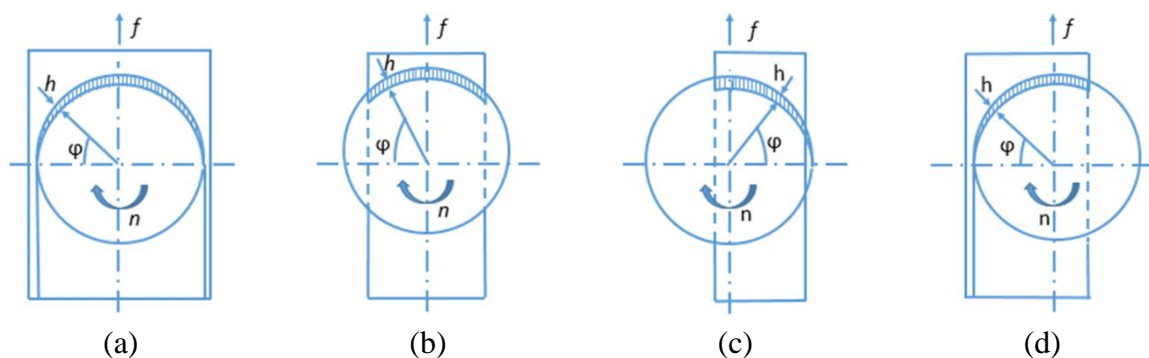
Tipos de fresamento frontal: (a) simétrico de rasgo; (b) simétrico comum; (c) assimétrico com toda superfície sendo fresada; (d) assimétrico [Diniz *et al.*, 2013].
